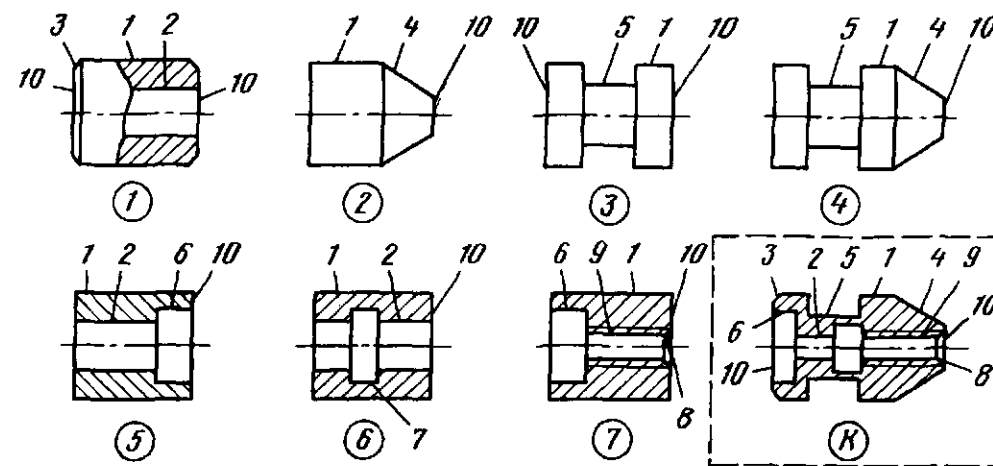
Создание комплексной детали: 1 – 7 – детали группы; 1 – 10 – элементарные обрабатываемые поверхности
